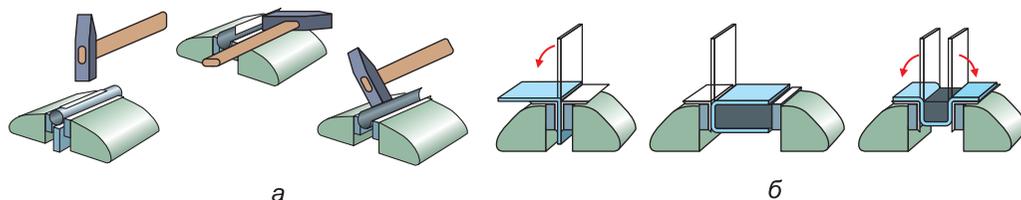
Гнутьё заготовки: а – цилиндрической формы; б – прямоугольной формы
